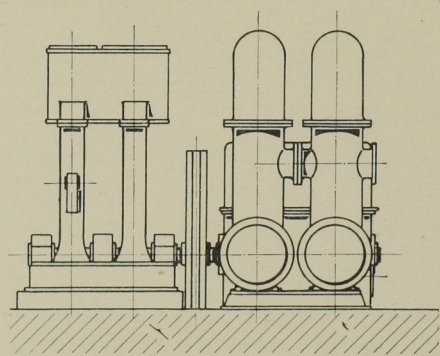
Stirnansicht der Pumpen samt Dampfmaschine.
